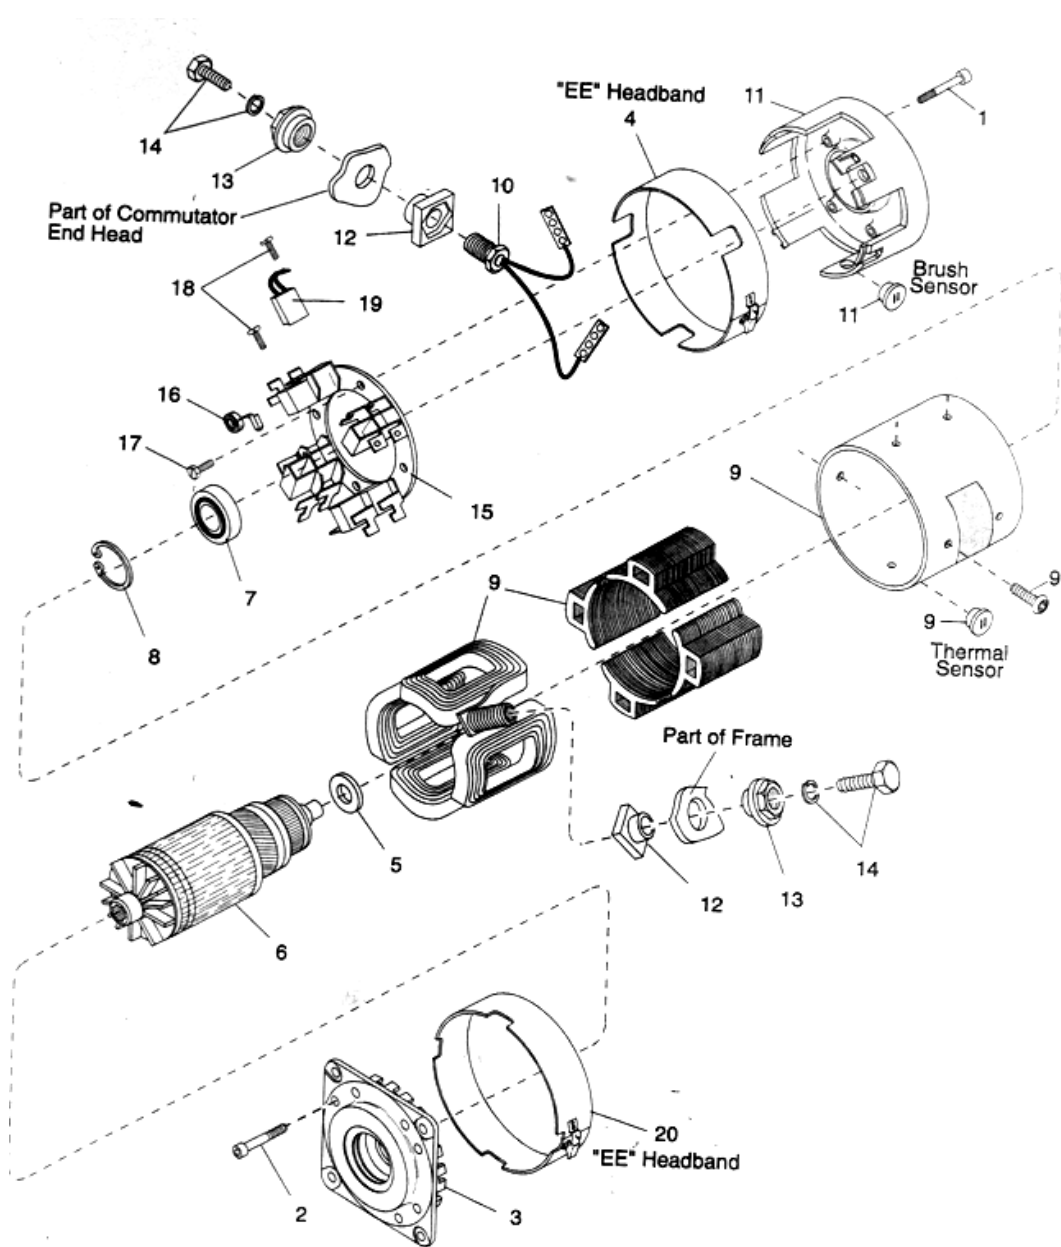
MOTOR DE TRACCION, LEVANTE Y ACCESORIOS
